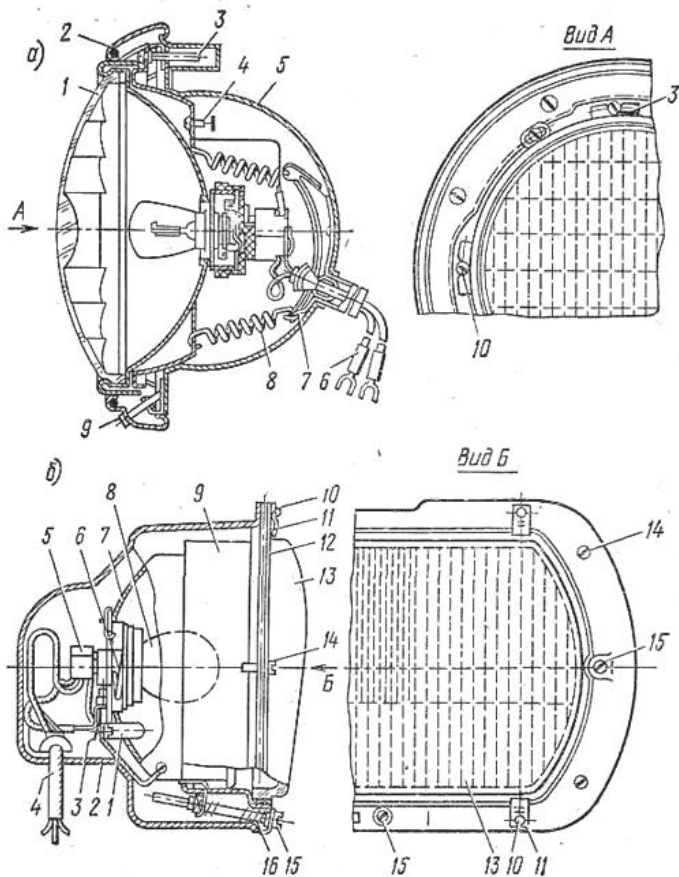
Фары: а – круглая; б – прямоугольная
